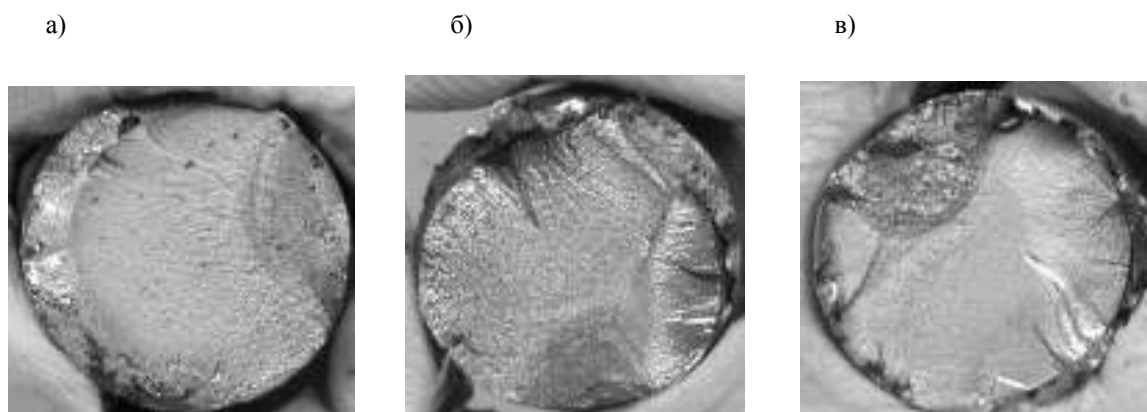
Поверхность усталостного излома образца из стали 45, наплавленного проволокой: а – ПП-Нп-80Х20РЗТ; б – 08Х13; в – У7
